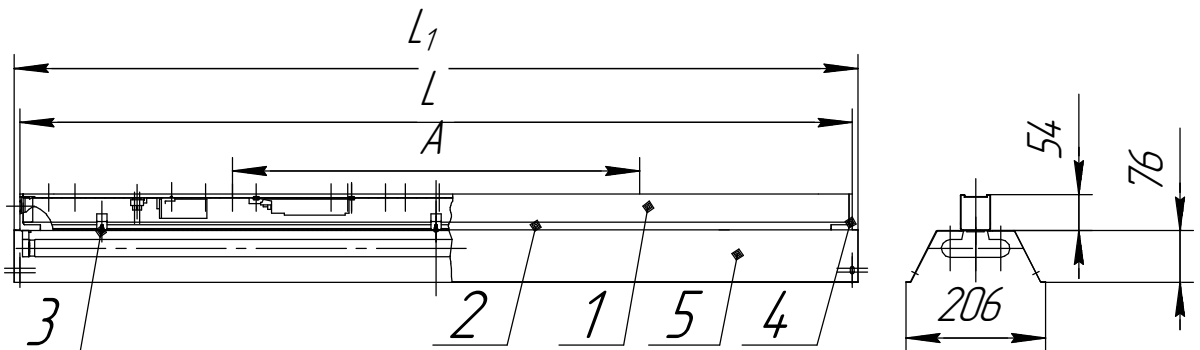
1. Корпус в сборе, 2. Крышка, 3. Винт, 4. Крышка, 5. Отражатель.
